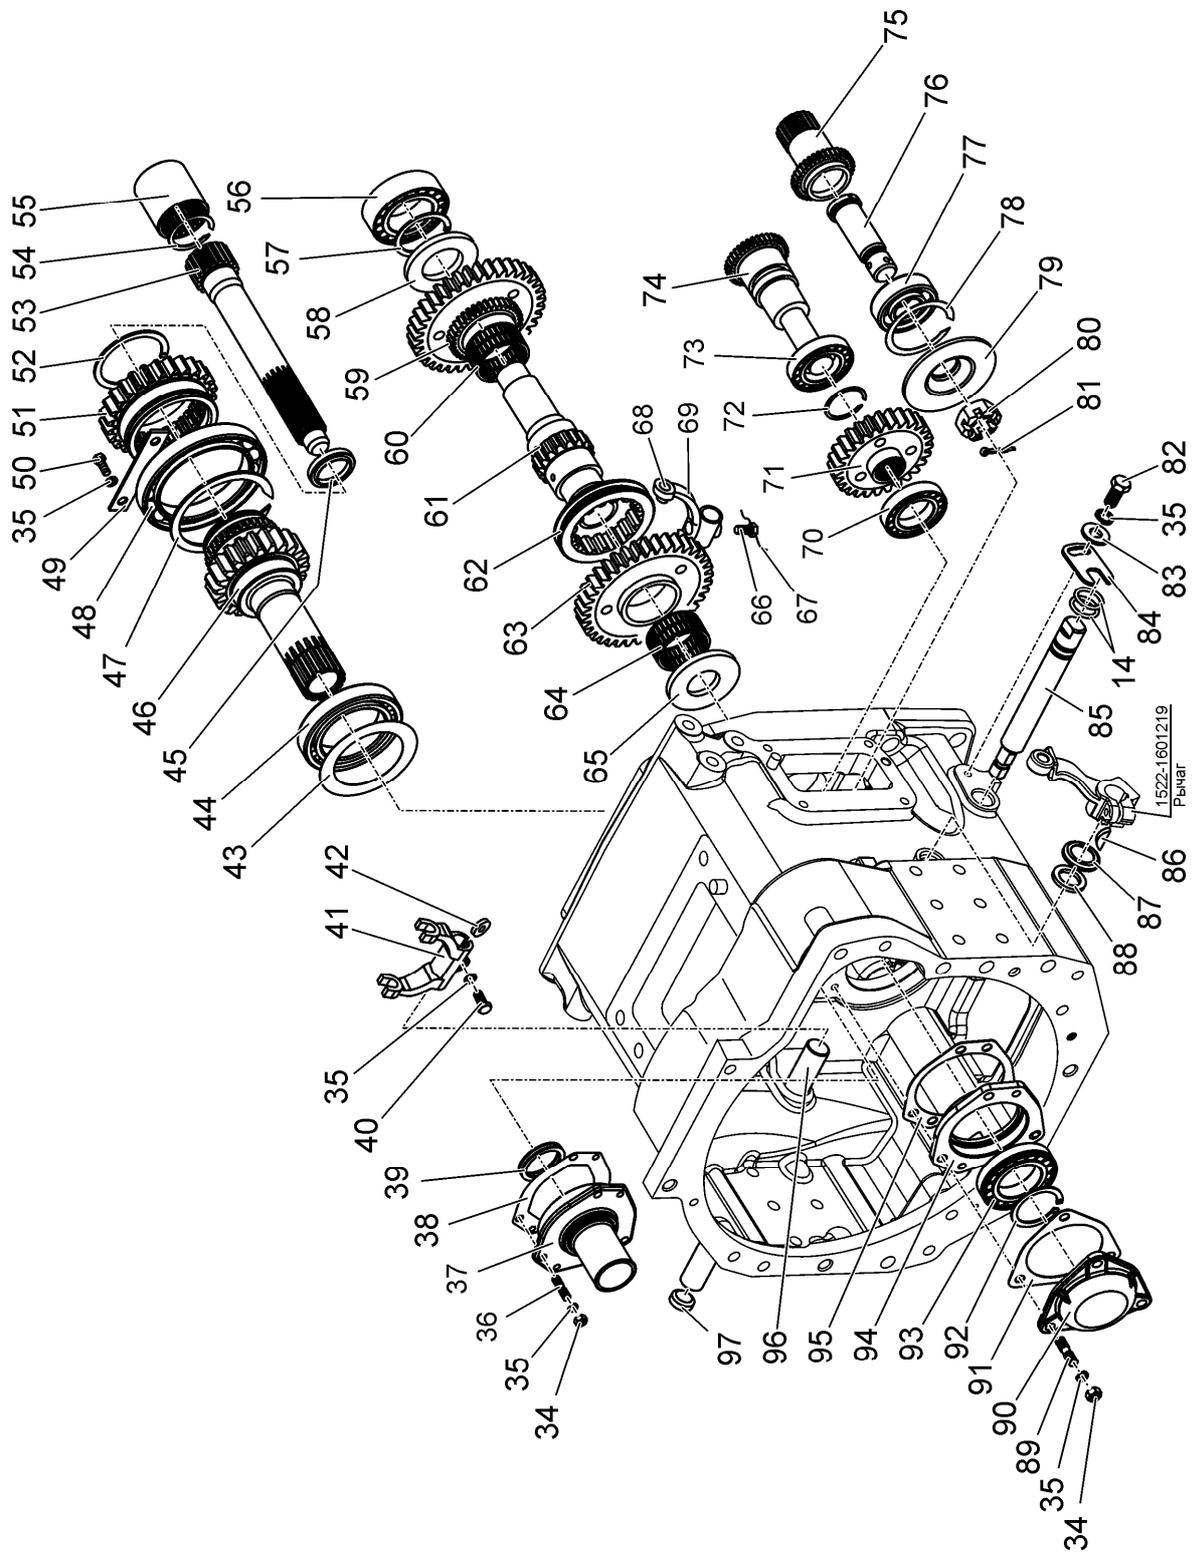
(лист 2 из 2) – Корпус сцепления. Горловина заливная. Шестерня. Кронштейн отводки. Вал. Втулка. Вилка. Вал-шестерня. Стакан
